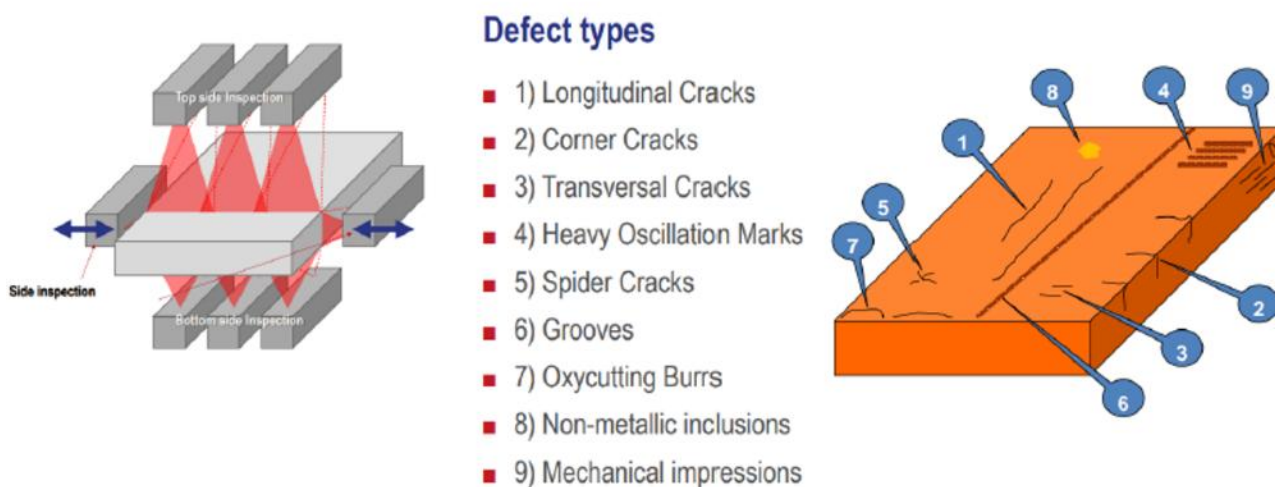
Автоматична система візуального контролю поверхні заготовки
